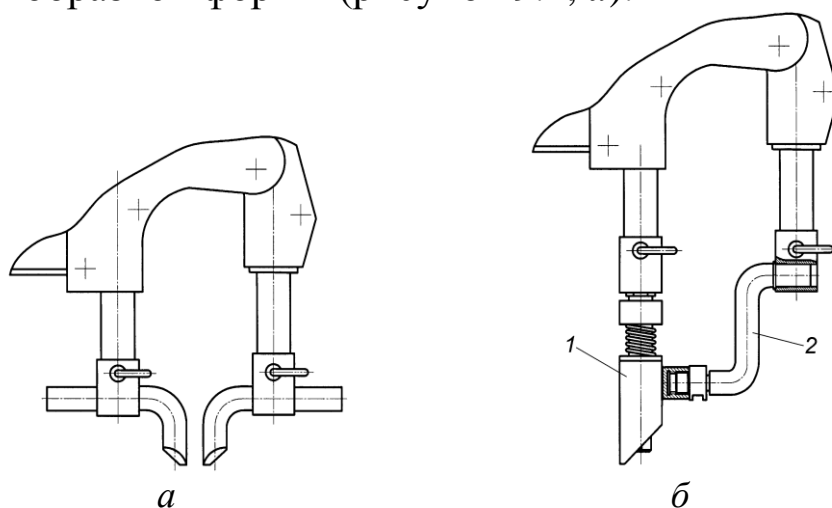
Крепление в клещах электродов для сварки с односторонним подводом тока (*а*) и специальной насадки для Т-образной сварки крепежа (*б*): *1* – насадка; *2* – гибкий токоподвод
